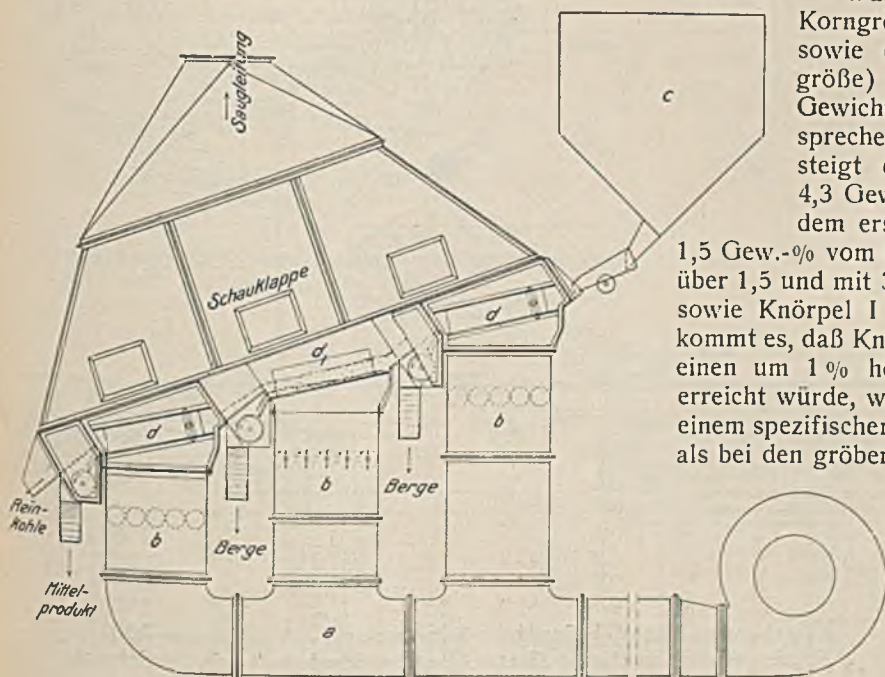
Pneumatische Setzmaschine Bauart Carlshütte.
